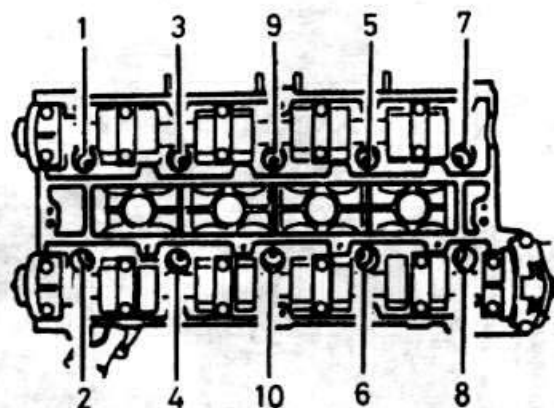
Последовательность ослабления болтов головки блока цилиндров — двигатель с двумя распредвалами
